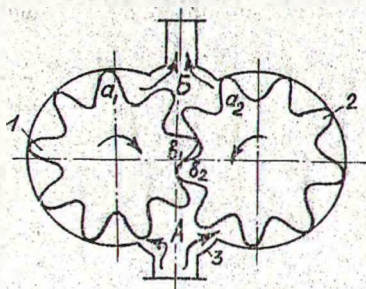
Схема шестеренчатого насоса: 1 — ведущая шестерня; 2 — ведомая шестерня; 3 — корпус насоса.
